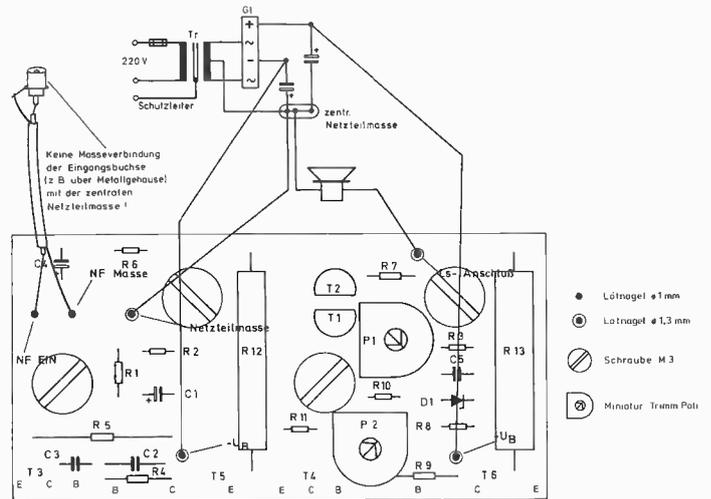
Der Verdrahtungsplan zeigt alle Verbindungen zur Außenwelt.
